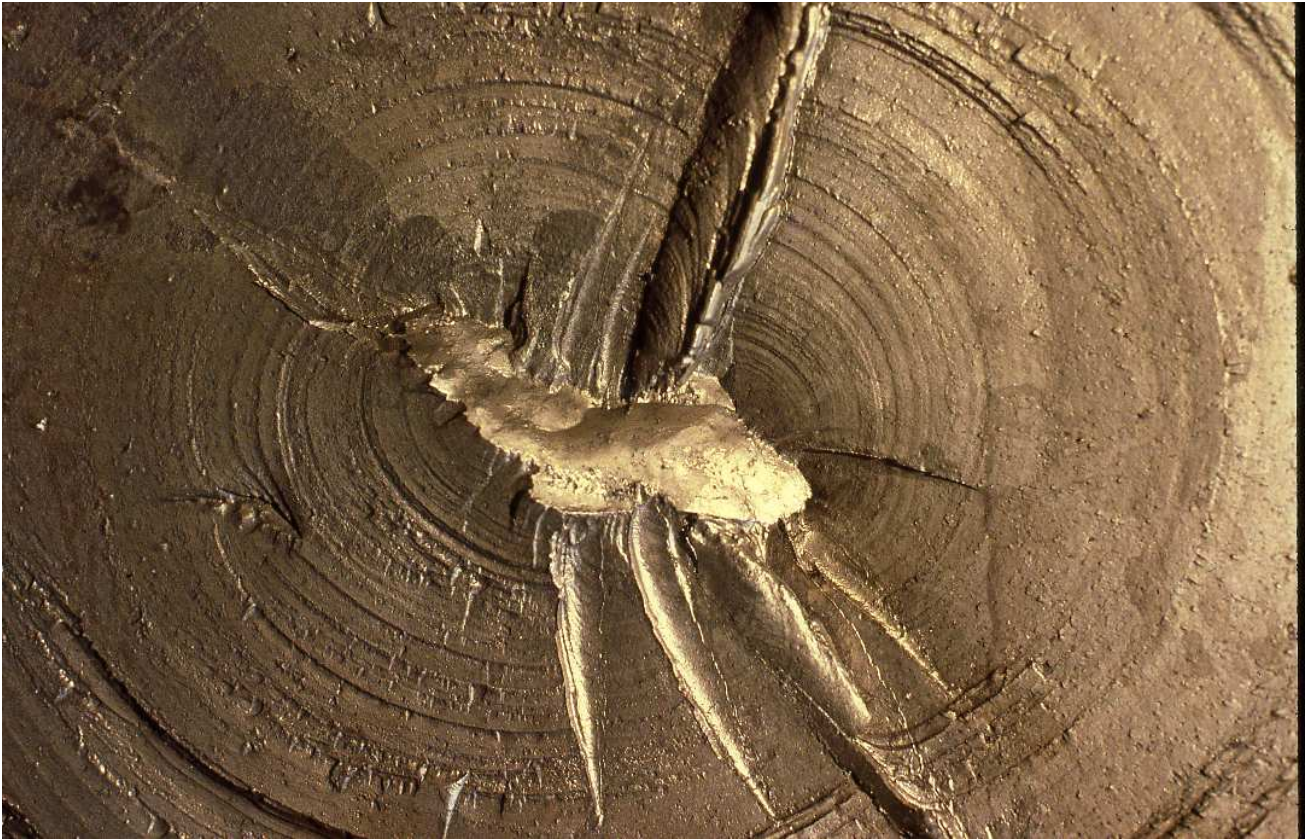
Ermüdungsbruch eines Hammerbären (Querriss im Oberbär mit gut erkennbaren „Rastlinien“); um 1990
